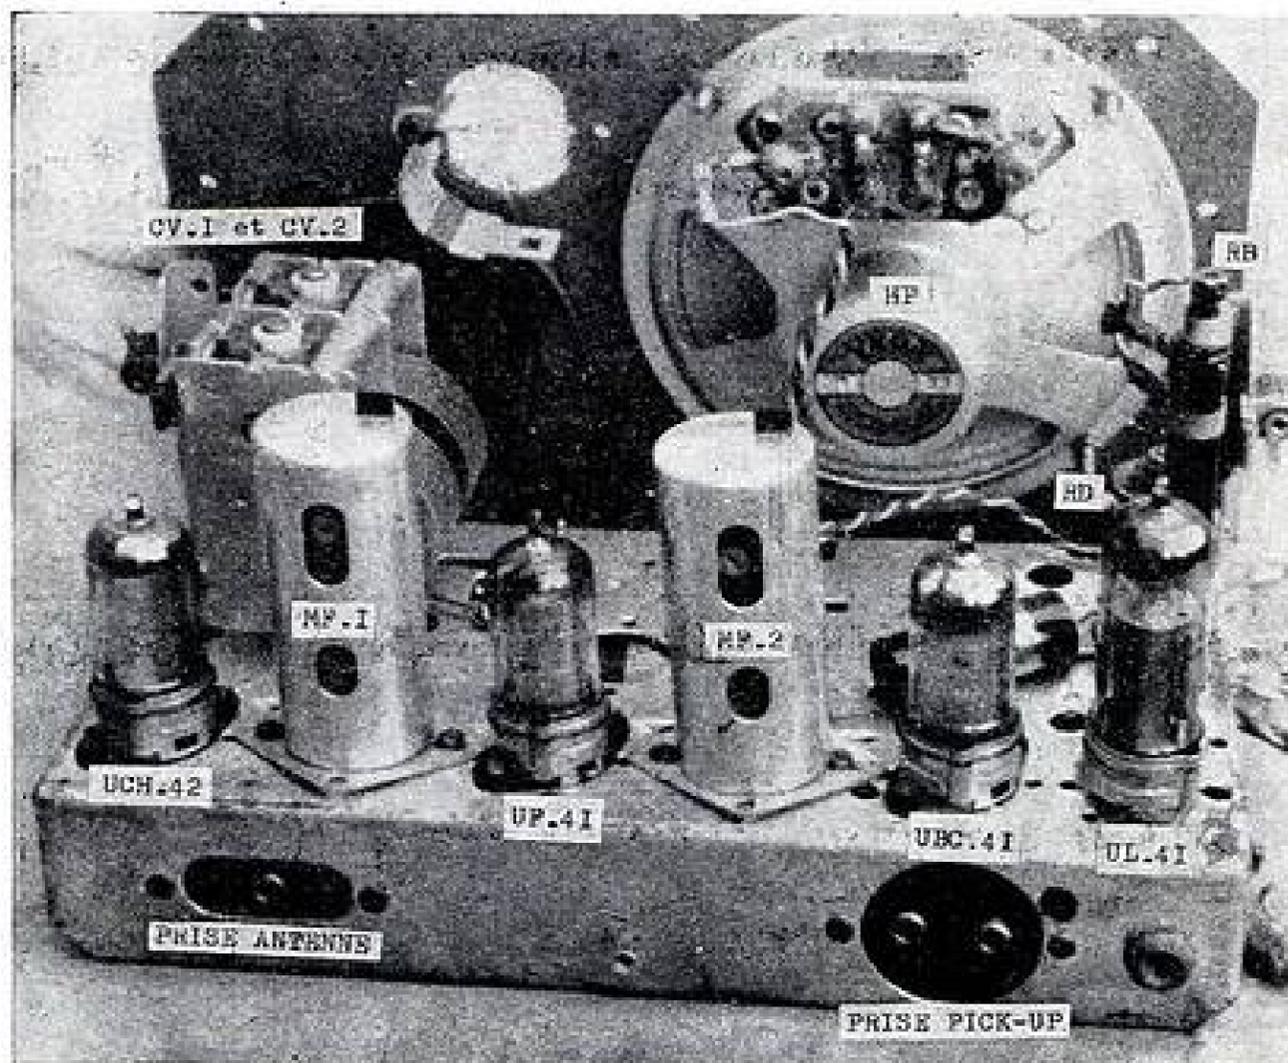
Disposition des pièces sur le dessus du châssis.
